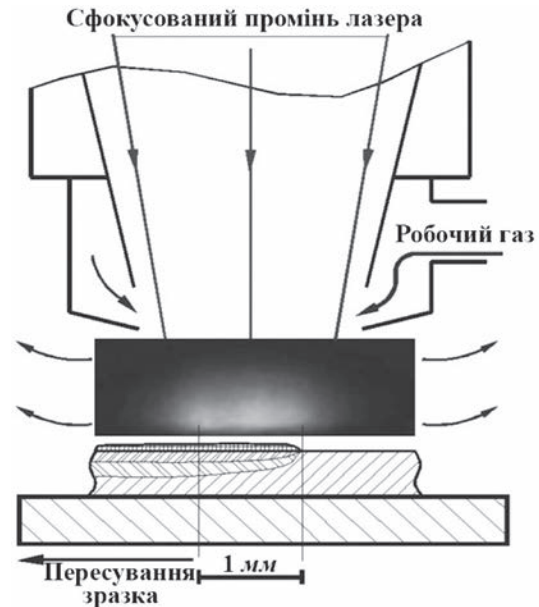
Схема лазерно-плазмової обробки металу із зображенням приповерхневої плазми оптичного пульсуючого розряду
